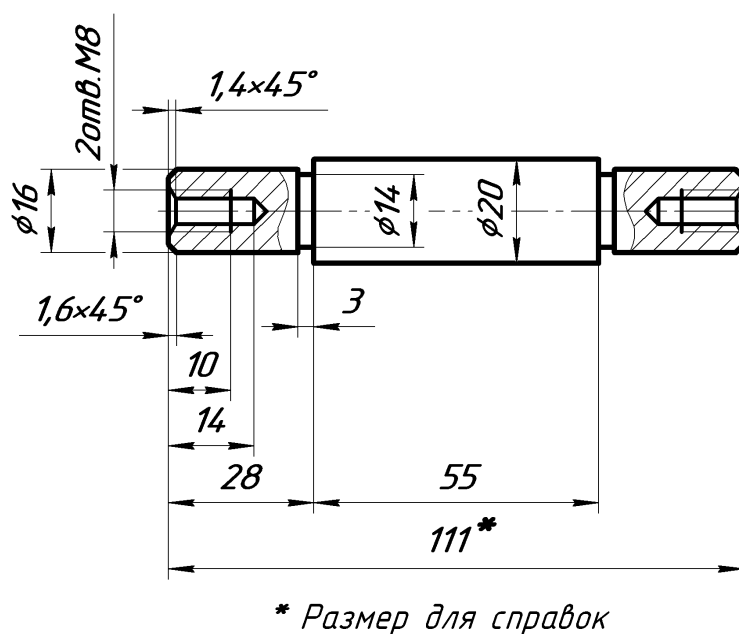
Нанесение размеров детали с одинаковыми элементами
